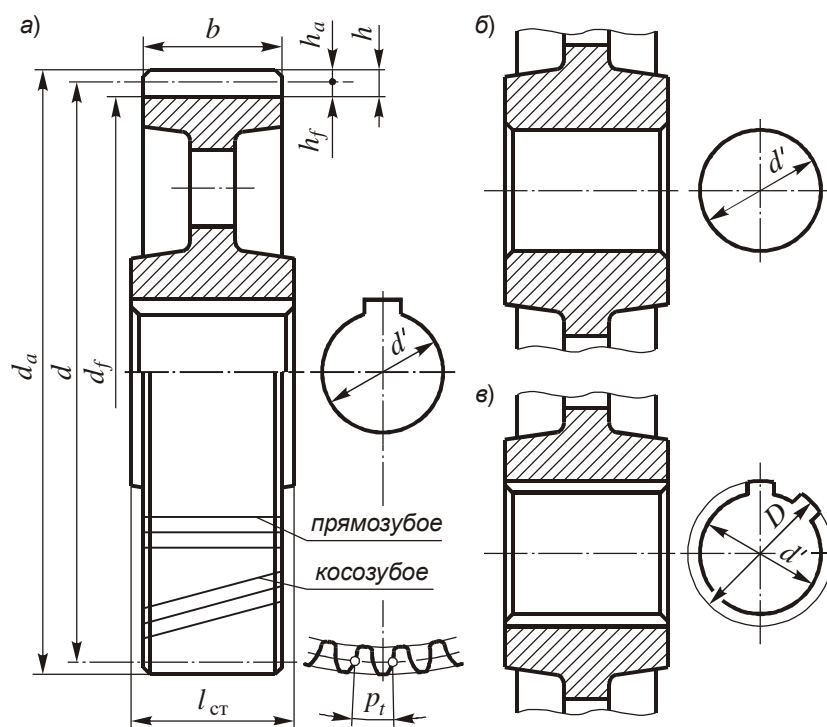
Эскиз зубчатого колеса: а – со шпоночным пазом; б – с гладким отверстием; в – с прямобочными шлицами
